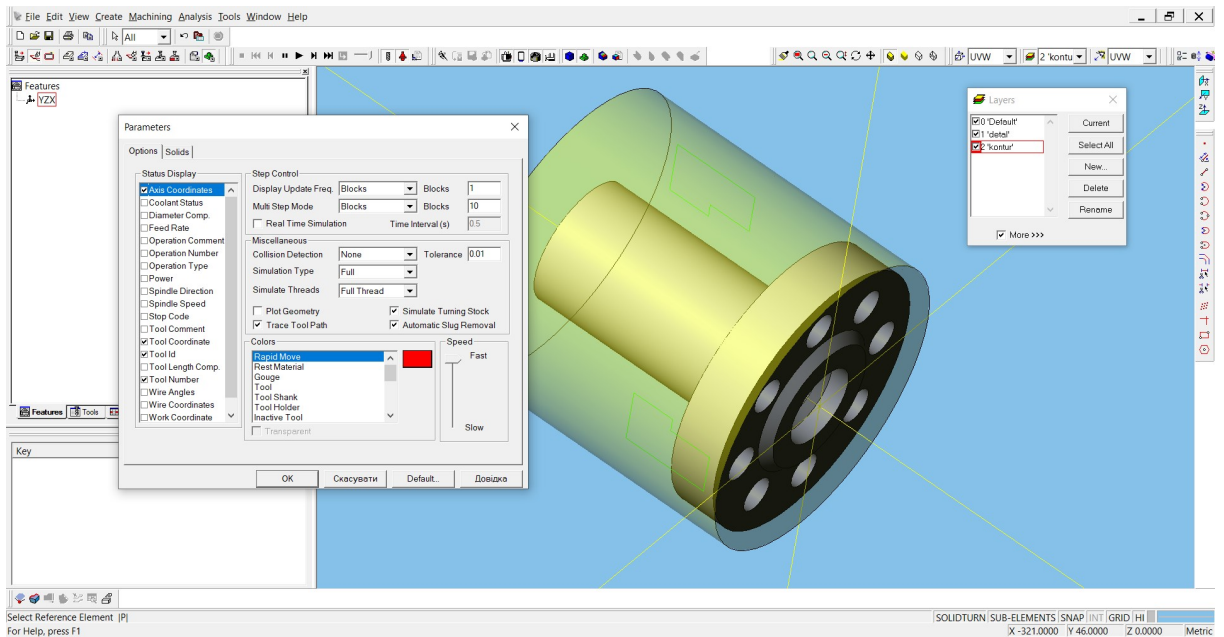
Створення заготовки деталі кришка у САМ Esprit
